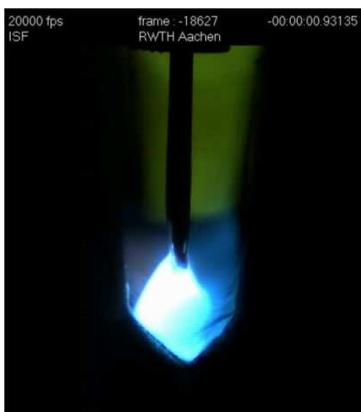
Schweißprozess, Steiflankennaht
